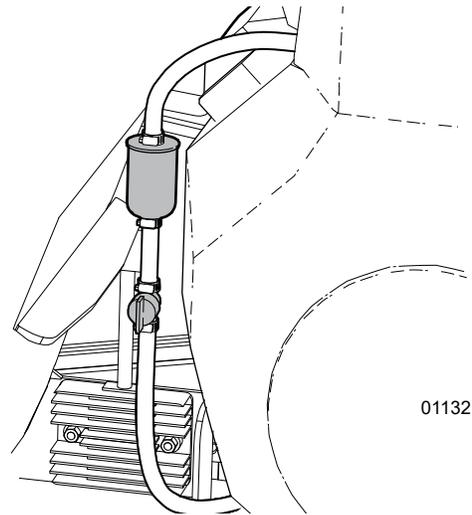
Filtre à carburant du moteur et robinet d'arrêt
